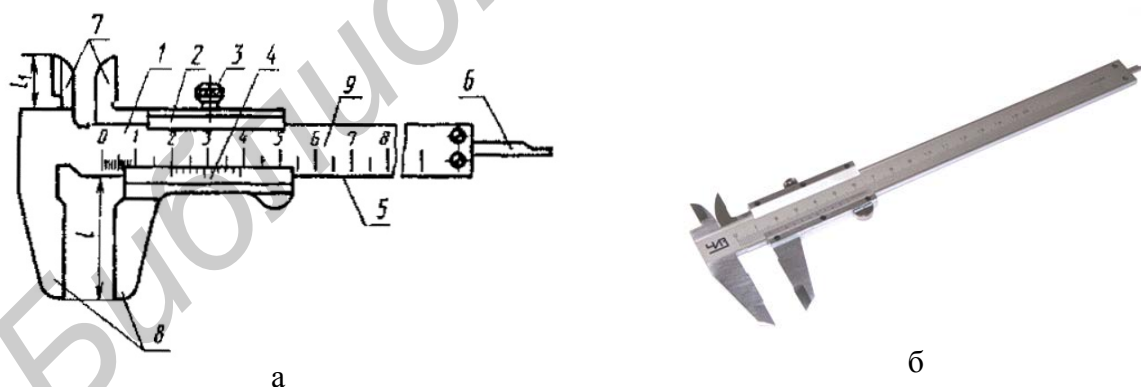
Конструкция и внешний вид двустороннего штангенциркуля
